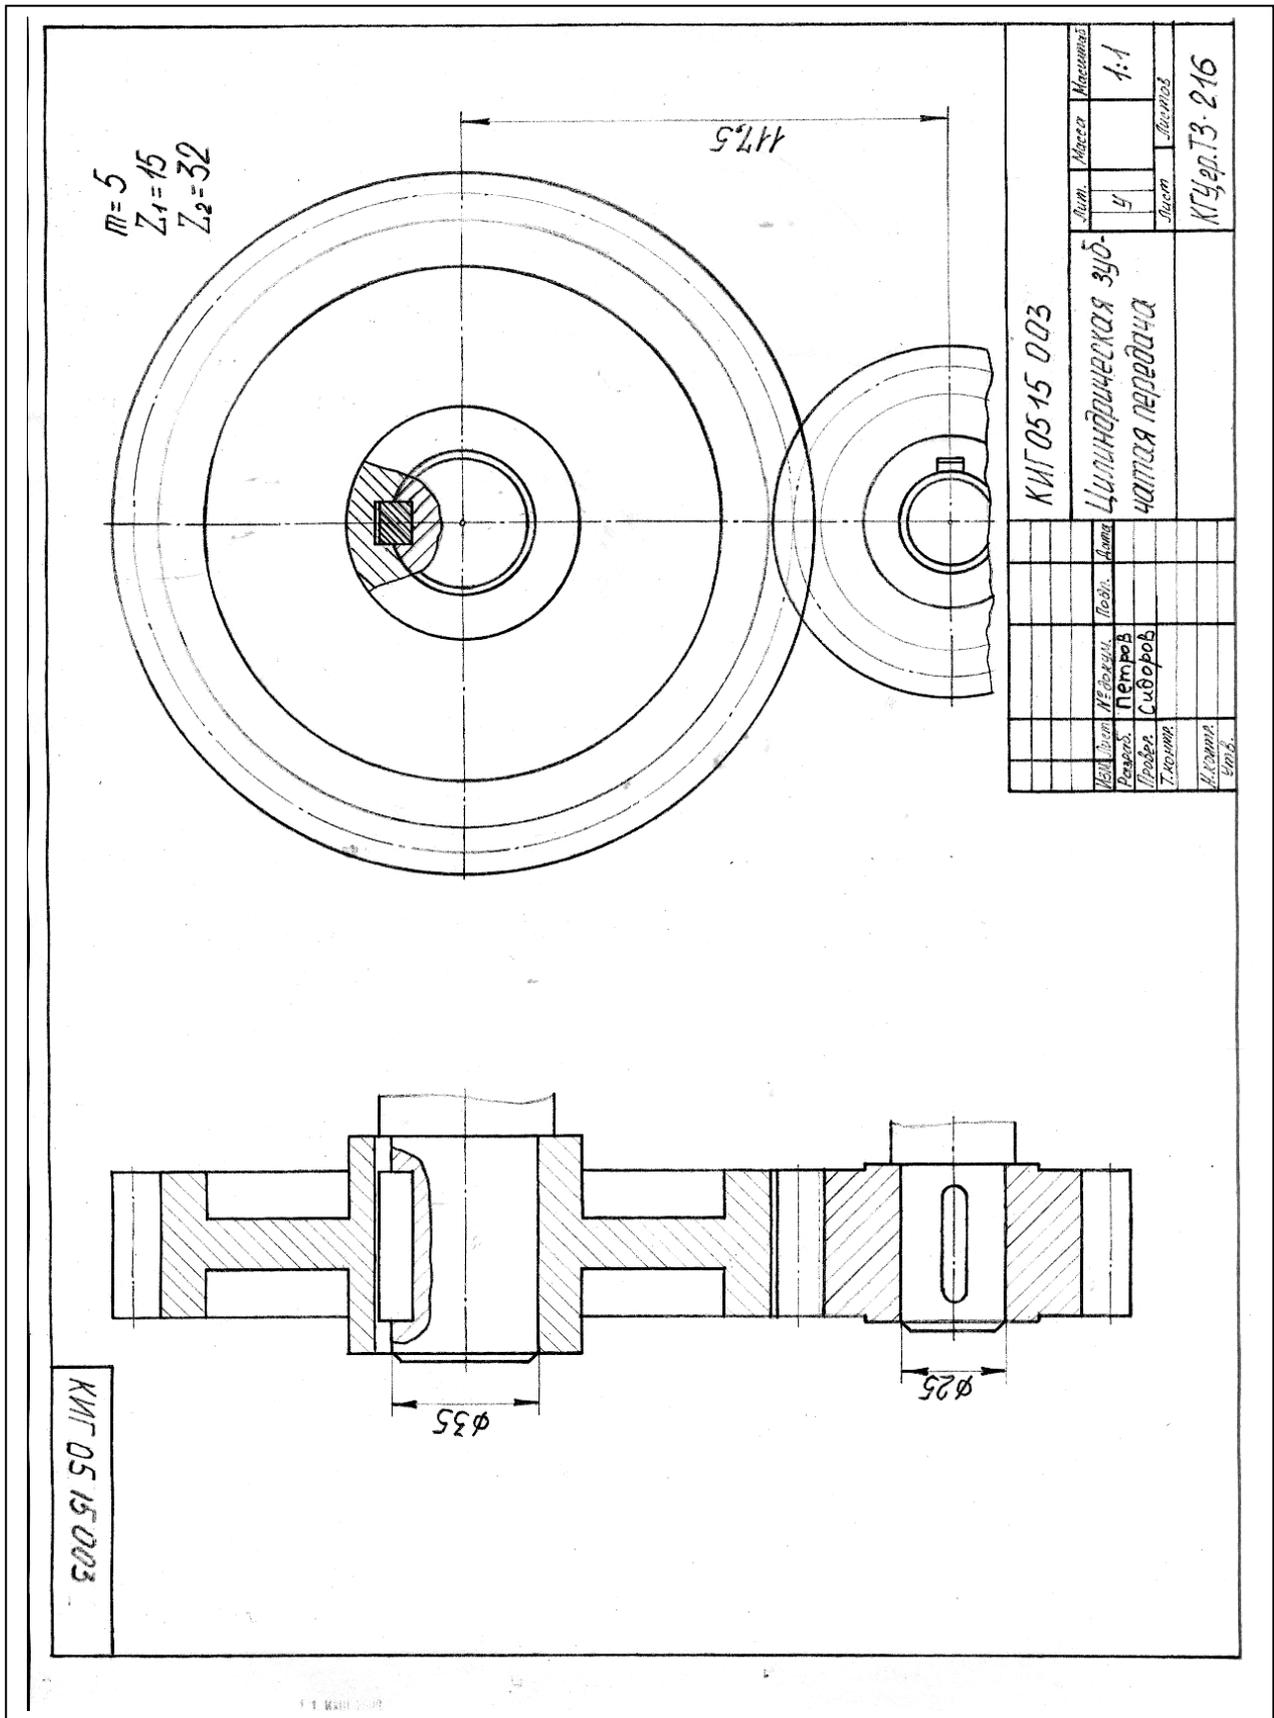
Чертеж цилиндрической зубчатой передачи
